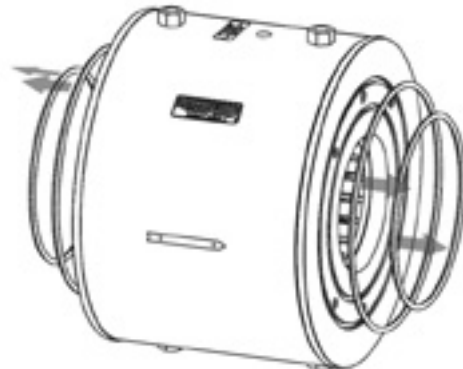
Entfernen Sie alle 4 O-Ringe der Abdeckplatte.
